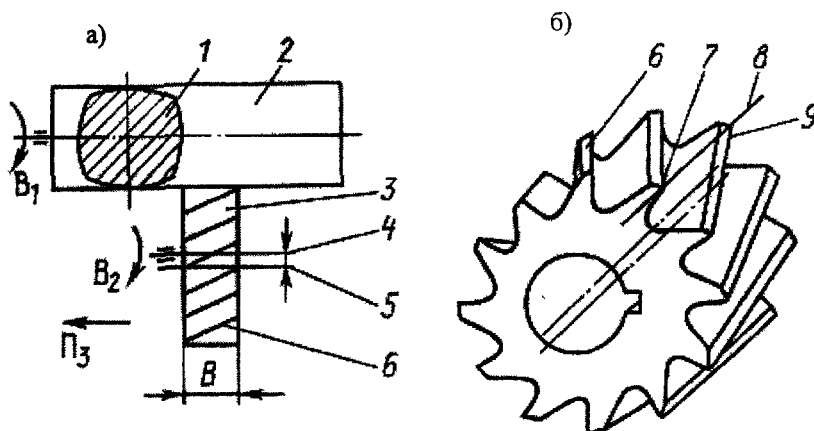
Формообразование некруглой поверхности дисковым инструментом с винтовым зубом:
